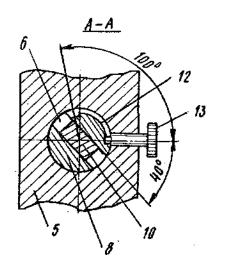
в - Устройство электрододержателя для сварки наклонным электродом
